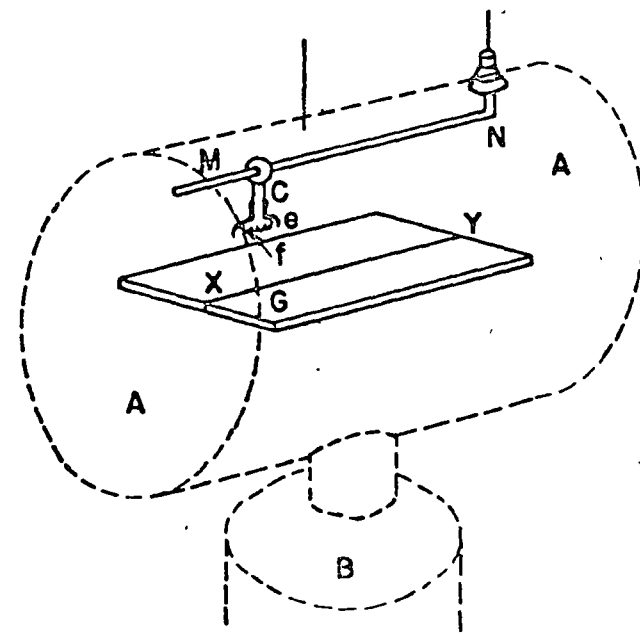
Principio del soldeo por bombardeo electrónico.
